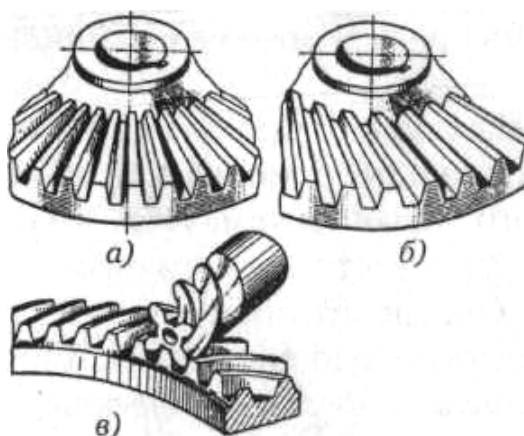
Конические зубчатые колеса: *а* — колесо с прямыми зубьями; *б* — колесо с косыми зубьями; *в* — колесо с круговыми зубьями
